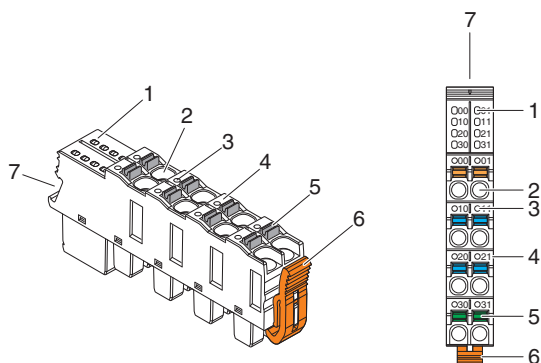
Prinzipieller Aufbau eines IndraControl S20-Steckers
